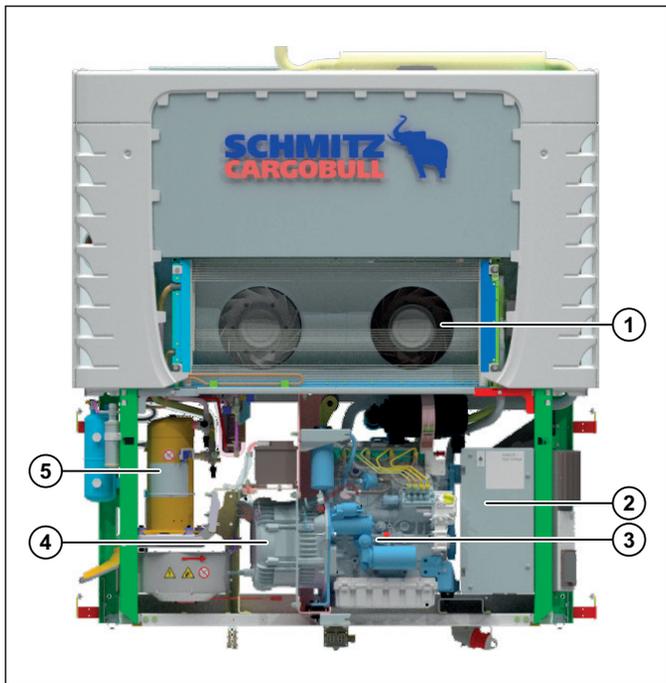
Вид с открытыми дверцами (S.CU d80)
